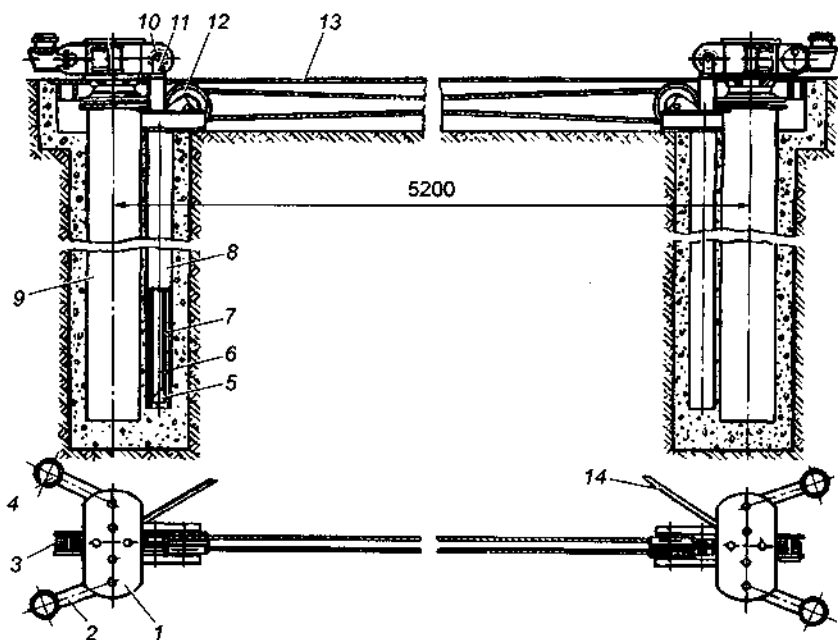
Двухплунжерный электрогидравлический подъемник П-111: 1 — плита платформы; 2 — балка платформы; 3 — барабан; 4 — подхват; 5 — четырехклиновый зажим троса; 6 — толкающая труба синхронизирующей стрелы; 7 — трос; 8 — кожух толкающей трубы; 9 — цилиндр в сборе; 10 и 12 — малый и большой блоки соответственно; 11 — предохранительный стержень; 13 — настил; 14 — маслопровод
